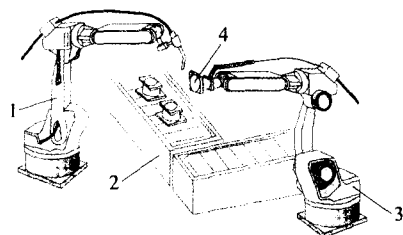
弧焊机器人与机器人式的焊件变位设备
